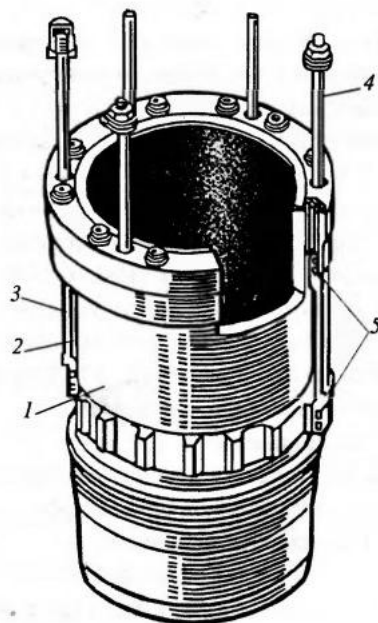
Втулка цилиндра дизеля Д49: 1 - втулка цилиндра; 2 - полость для воды; 3 - рубашка втулки; 4 - шесть шпилек крепления втулки к крышке цилиндра; 5- уплотнительное кольцо.
